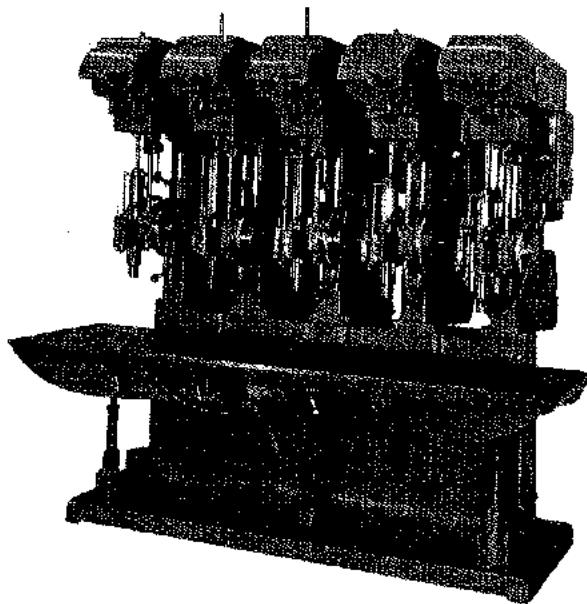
Taladradora múltiple de husillos independientes (Fosdick Machine Tool Co.)
